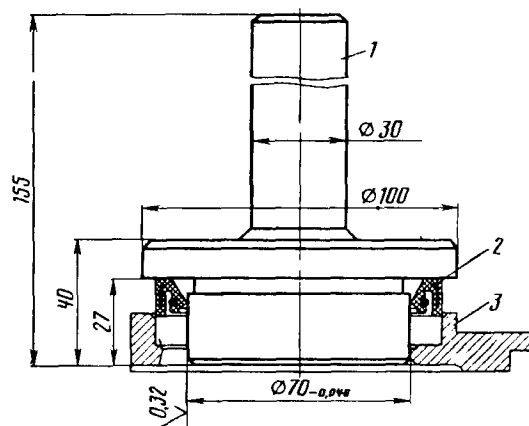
Запрессовка манжеты в держатель заднего подшипника коленчатого вала:
